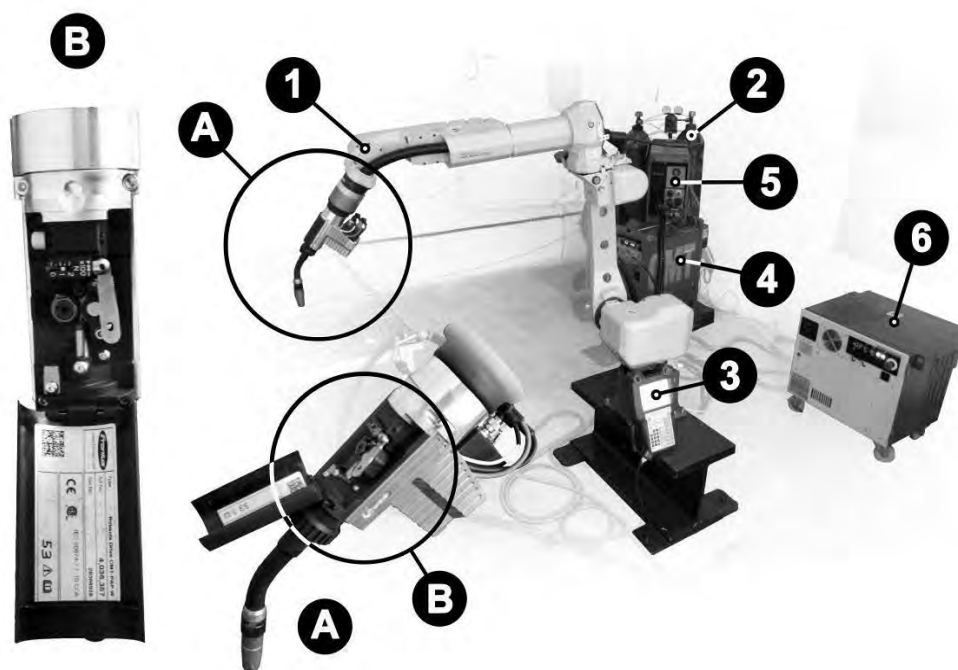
Оборудование для проведения экспериментальных исследований по аддитивной наплавке: А – интегрированная сварочная горелка с подающим приводом; В – механизм реверсивной подачи проволоки Robacta Drive CMT; 1 – сварочный робот FANUC ARC Mate 100iC; 2 – баллоны с защитным газом; 3 – пульт управления роботом FANUC Robot ARC Mate 100iC; 4 – источник питания Fronius TPS 3200 с системой CMT; 5 – подающий механизм; 6 – контроллер SYSTEM R-30iB
